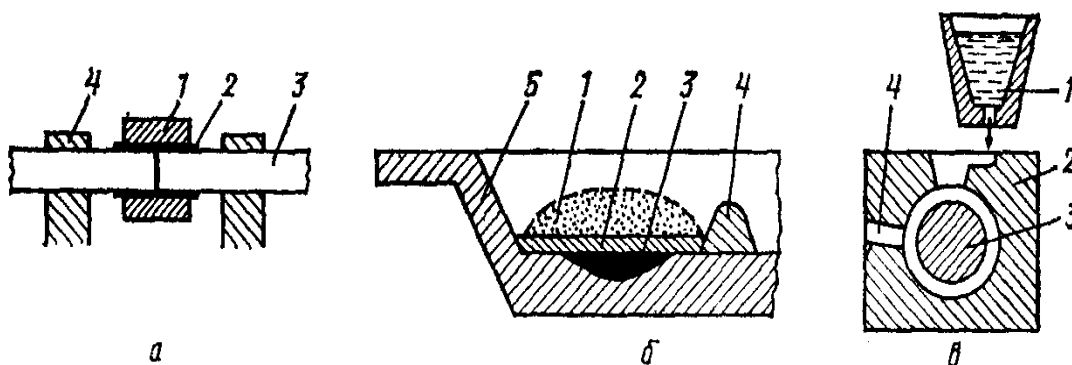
Варианты способа термитной сварки плавлением:
